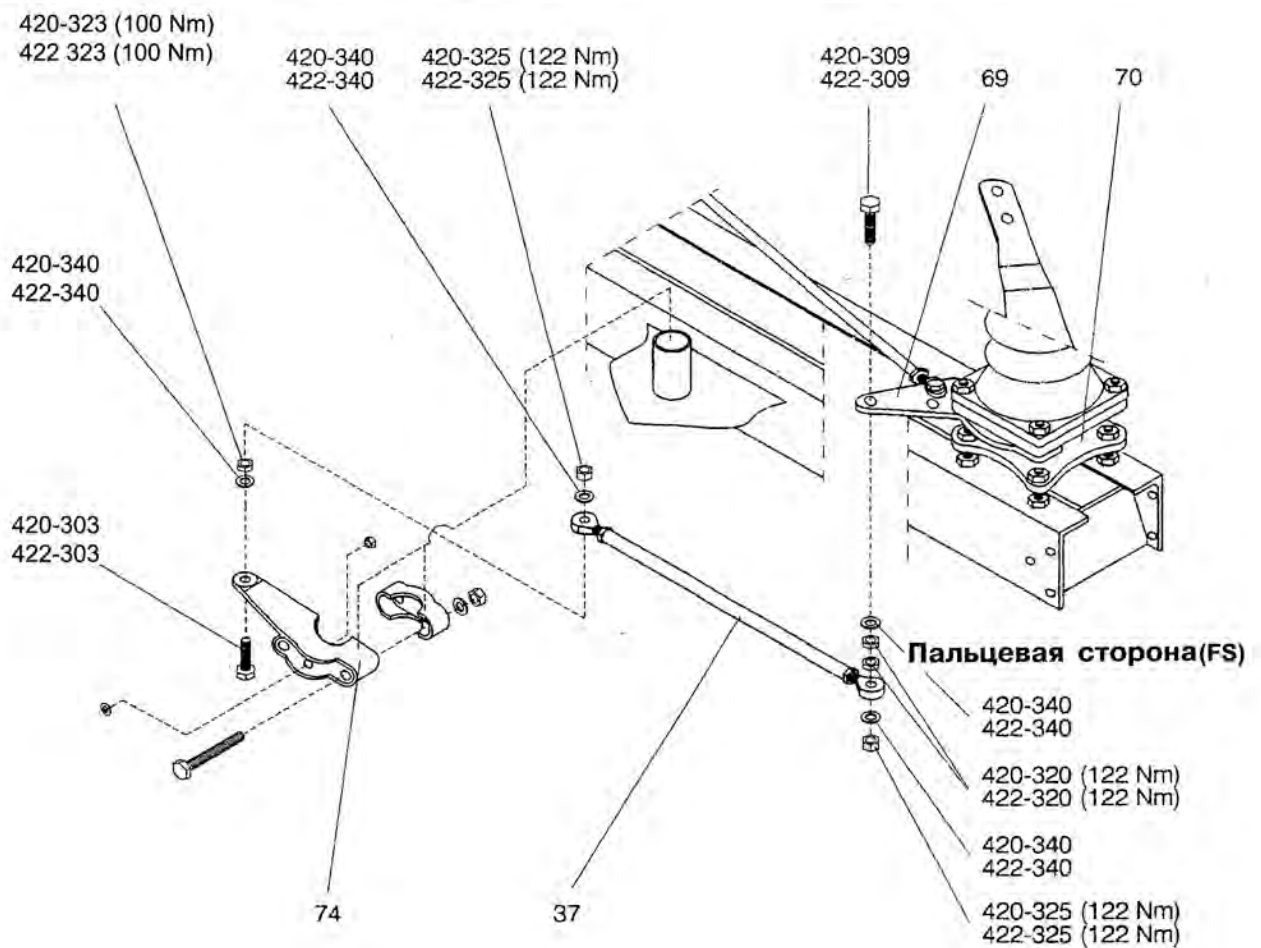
Установка тяг разъединителя: установка приводной тяги (37) при расположении приводного механизма разъединителя на стороне открывания
